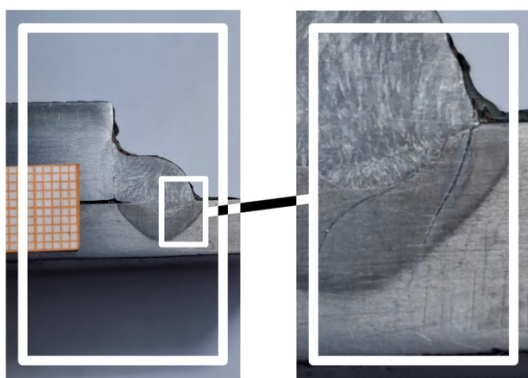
Трещина в нахлесточном сварном соединении
